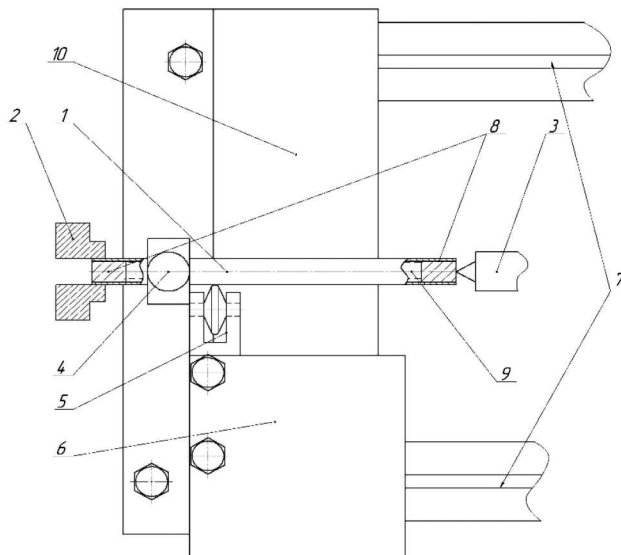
Схема роликового обкочування гвинтоподібних труб з використанням протитиску:
